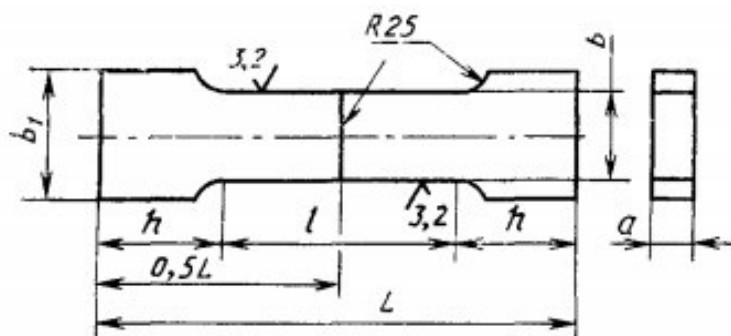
Форма и размеры плоских образцов для испытания стыковых соединений на статическое растяжение: a – толщина основного металла, a_1 – толщина образца, b – ширина рабочей части образца, b_1 – ширина захватной части образца, l – длина рабочей части образца, L – общая длина образца, h – длина захватной части образца
